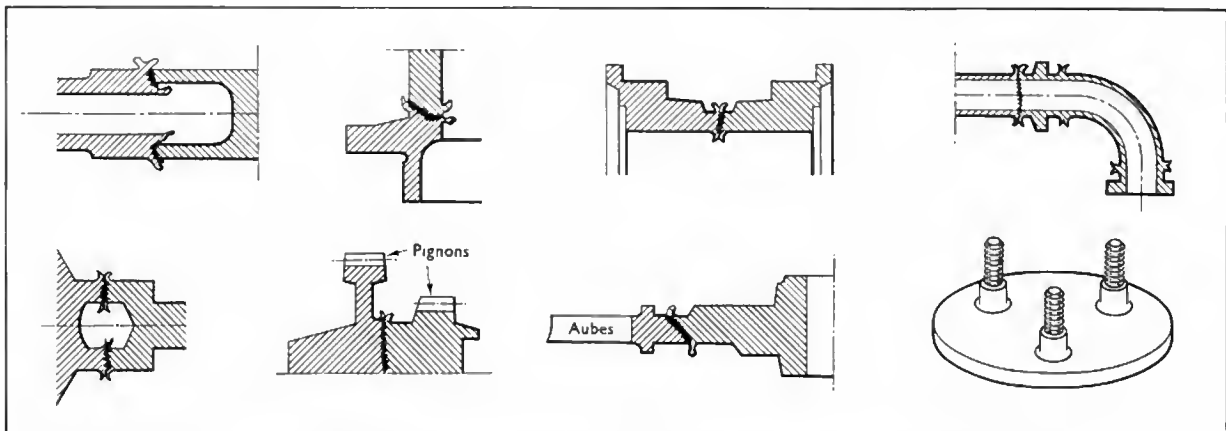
Quelques exemples de pièces soudées par friction (d'après document Carterpillar)
